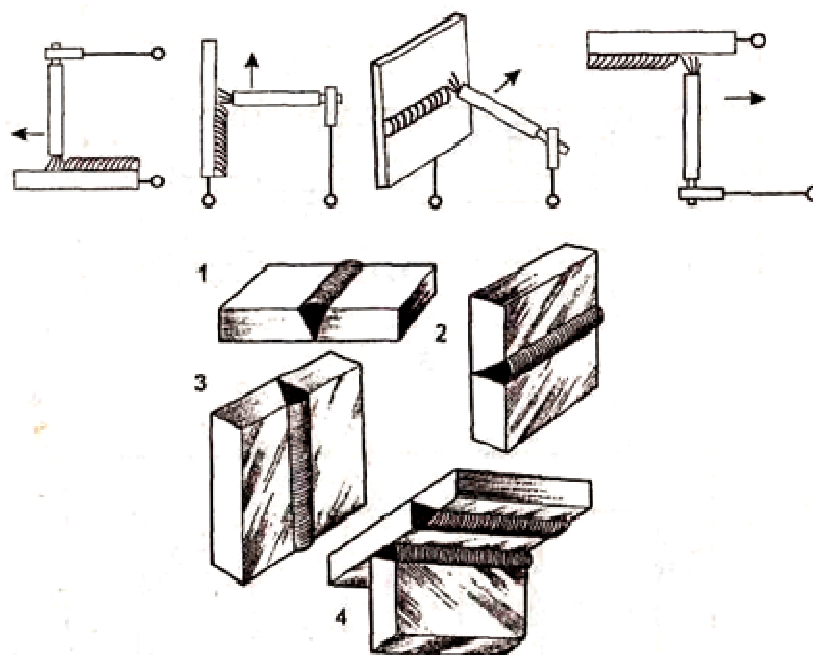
Основные положения сварных швов в пространстве:
